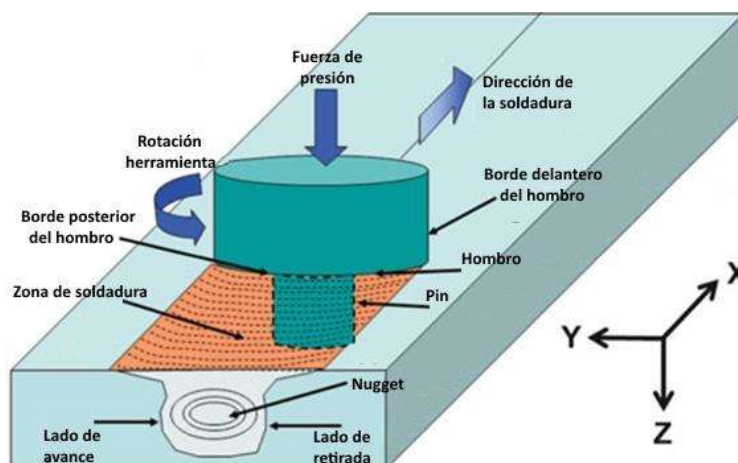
Principales componentes del proceso de soldadura por fricción-agitación [19].
